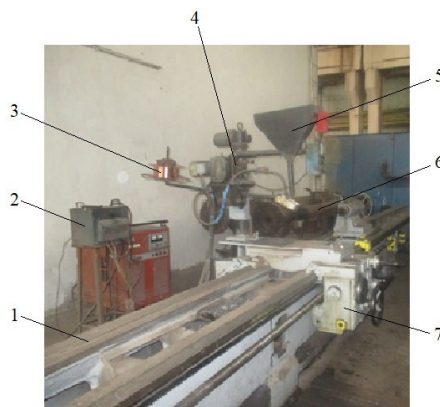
Установка автоматичного зварювання під шаром флюсу:
